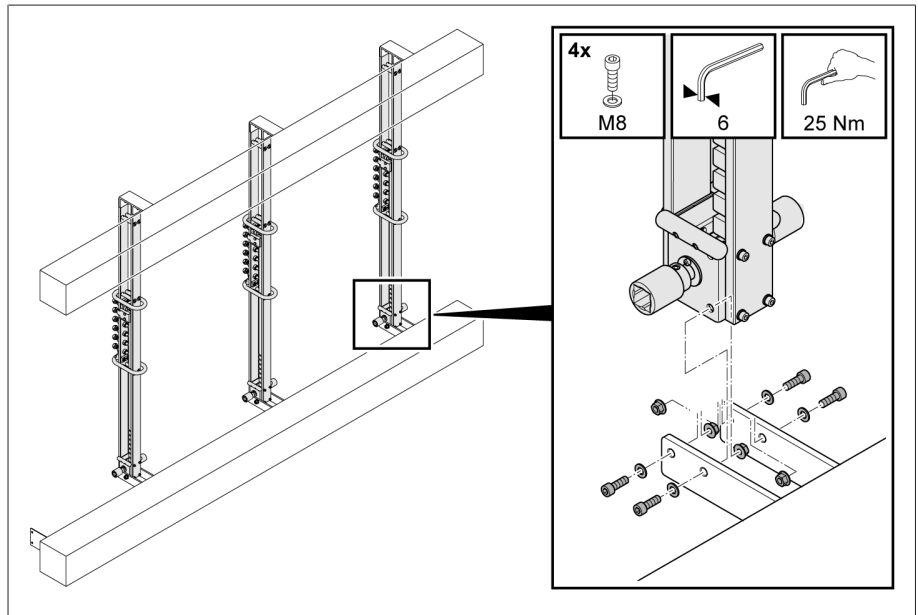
Getriebestufe befestigen, Umsteller mit frontal angebrachten Kontakten
